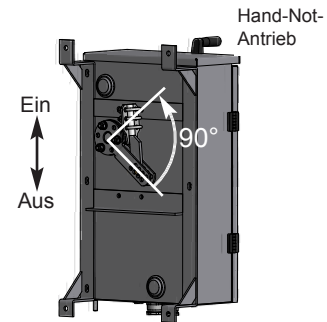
Drehsinn am UM 90, Darstellung des Gehäuses aus rückseitiger Ansicht!
